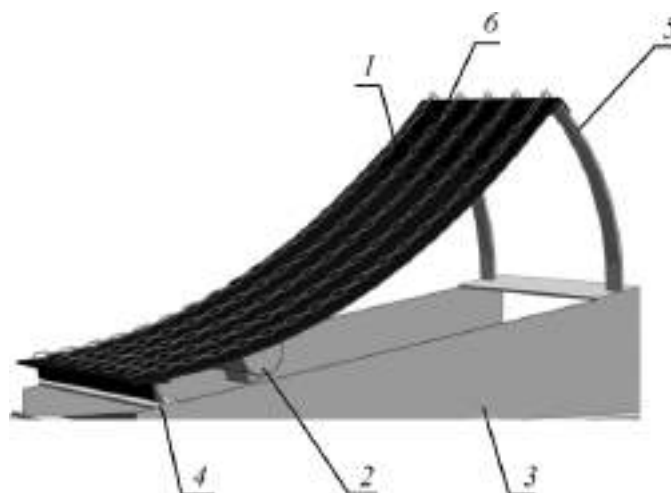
Вибрационный питатель: 1 — рабочий орган; 2 — вибровозбудитель; 3 — опорная рама; 4, 5 — упругие опорные элементы разгрузочного и загрузочного участков рабочего органа соответственно; 6 — гибкие подвижные элементы
